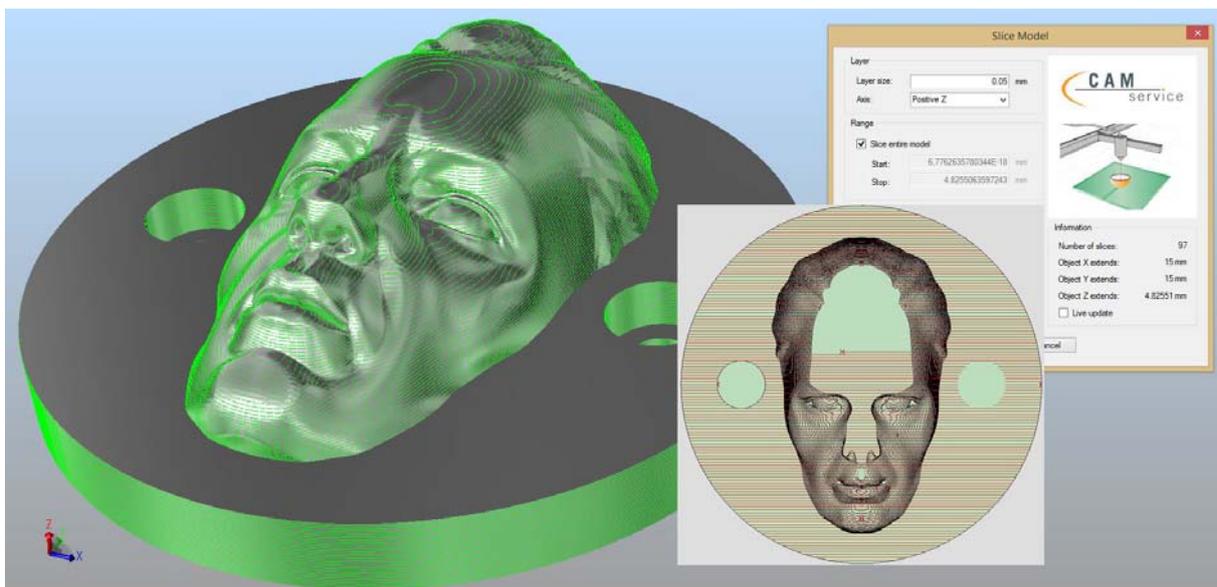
Werkzeugbahn-Optimierung mit Hilfe von Anschnitten, Zerstörschleifen und ‚Sky-writing‘ mit CAGILA® 3D
